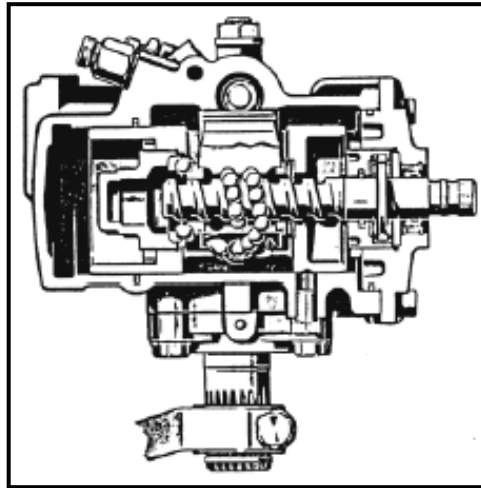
Mecanismo de dirección hidráulica de bolas recirculantes integradas
